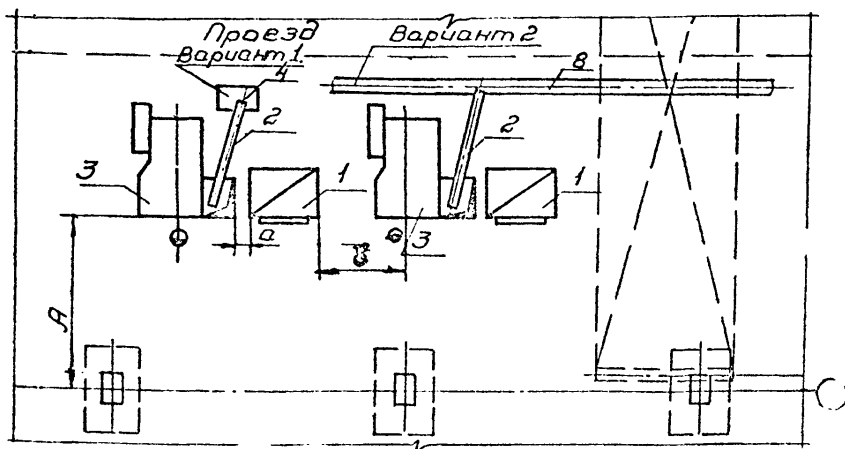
Схема расположения штатповочных линий на базе ГКМ:
